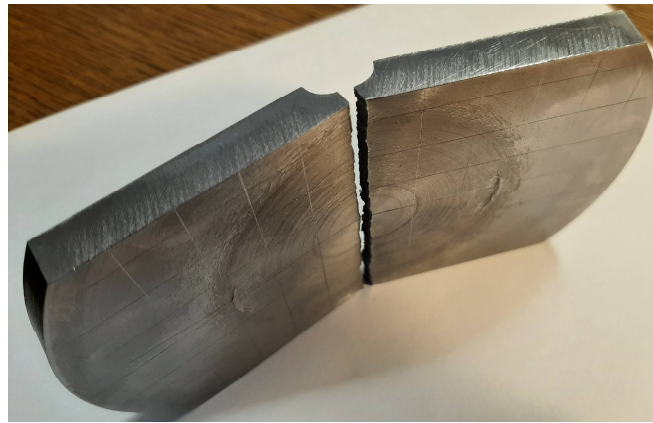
Разрушенный усеченный дисковый образец из первой группы:
